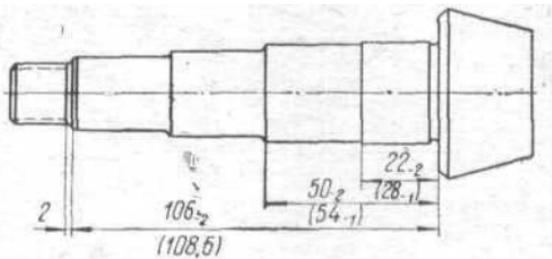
Размеры (без скобок) для дополнительной обработки вала ведущей шестерни главной передачи
